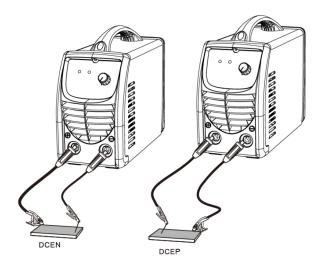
Anschluss für Lichtbogenhandschweißen
